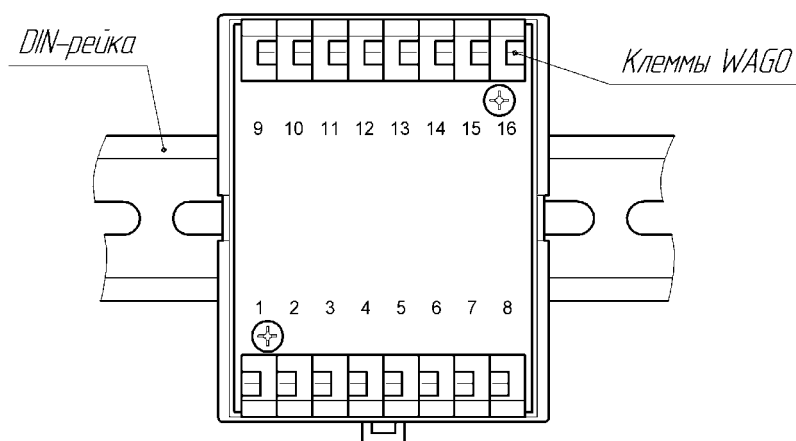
Вид модулей грозозащиты в корпусе без верхней крышки (ГЗС/Д и ГЗКС/Д)
